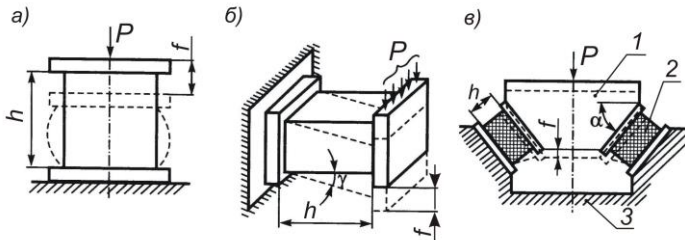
Схемы нагружения резиновых рессор:
